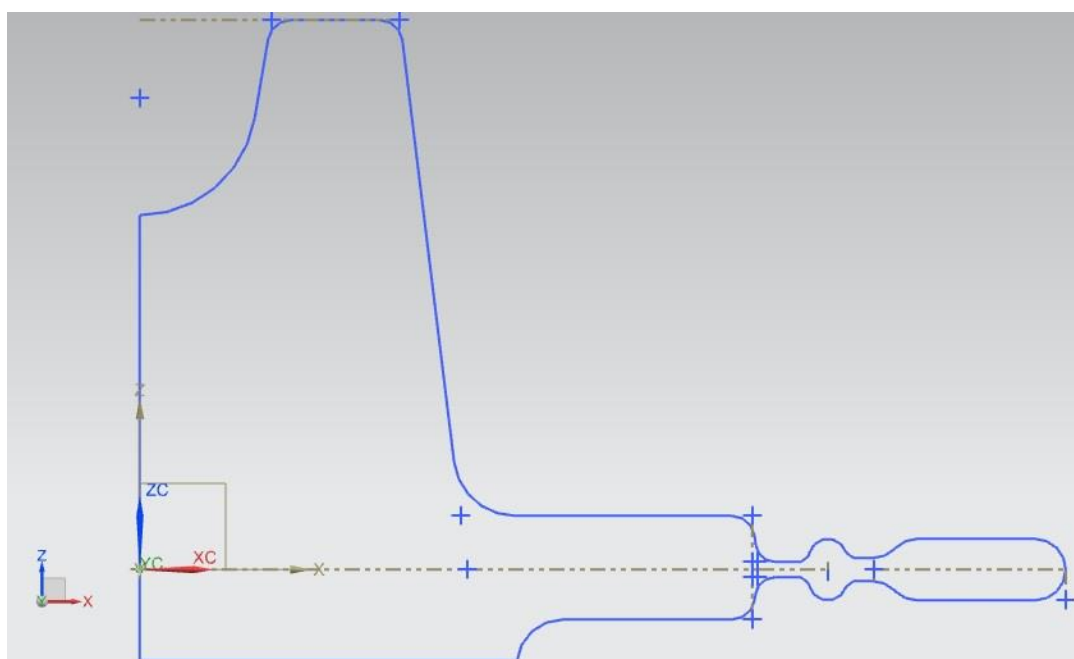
Ескіз гарячої заготовки з додаванням геометрії облойного рівчака V типу
